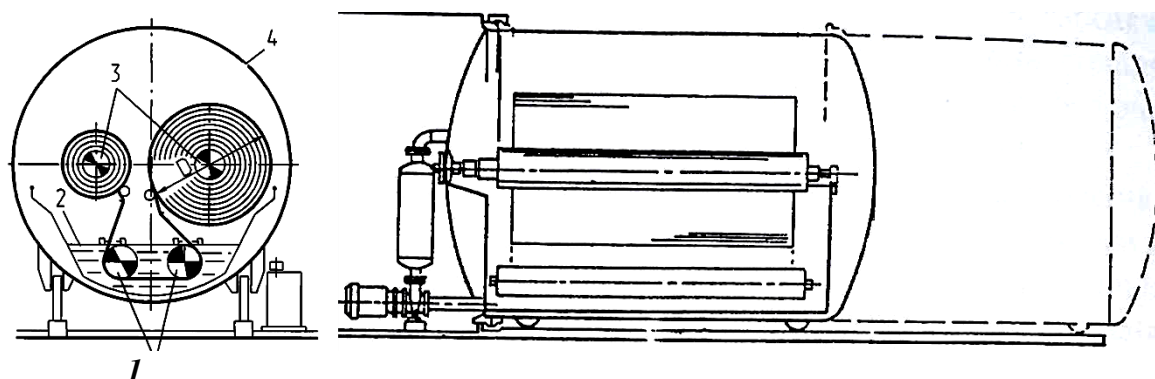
Схема джиггера крашения под давлением HD618-1200: 1 – ролики; 2 – раствор красителя; 3 – тянущие валы с тканью; 4 – корпус.
